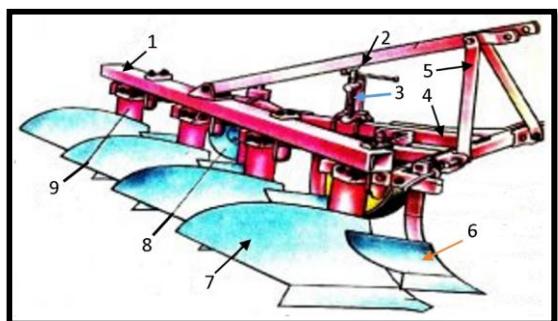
Общий вид плуга навесного ПЛН-4-35: 1 – главный брус рамы; 2 – распорка навесного устройства; 3 – механизм управления опорно-ходовым колесом; 4 – рама; 5 - рамка навесного устройства; 6 – предплужник; 7 – корпус; 8 - колесо опорно-регулировочное; 9 – стойка корпуса.
